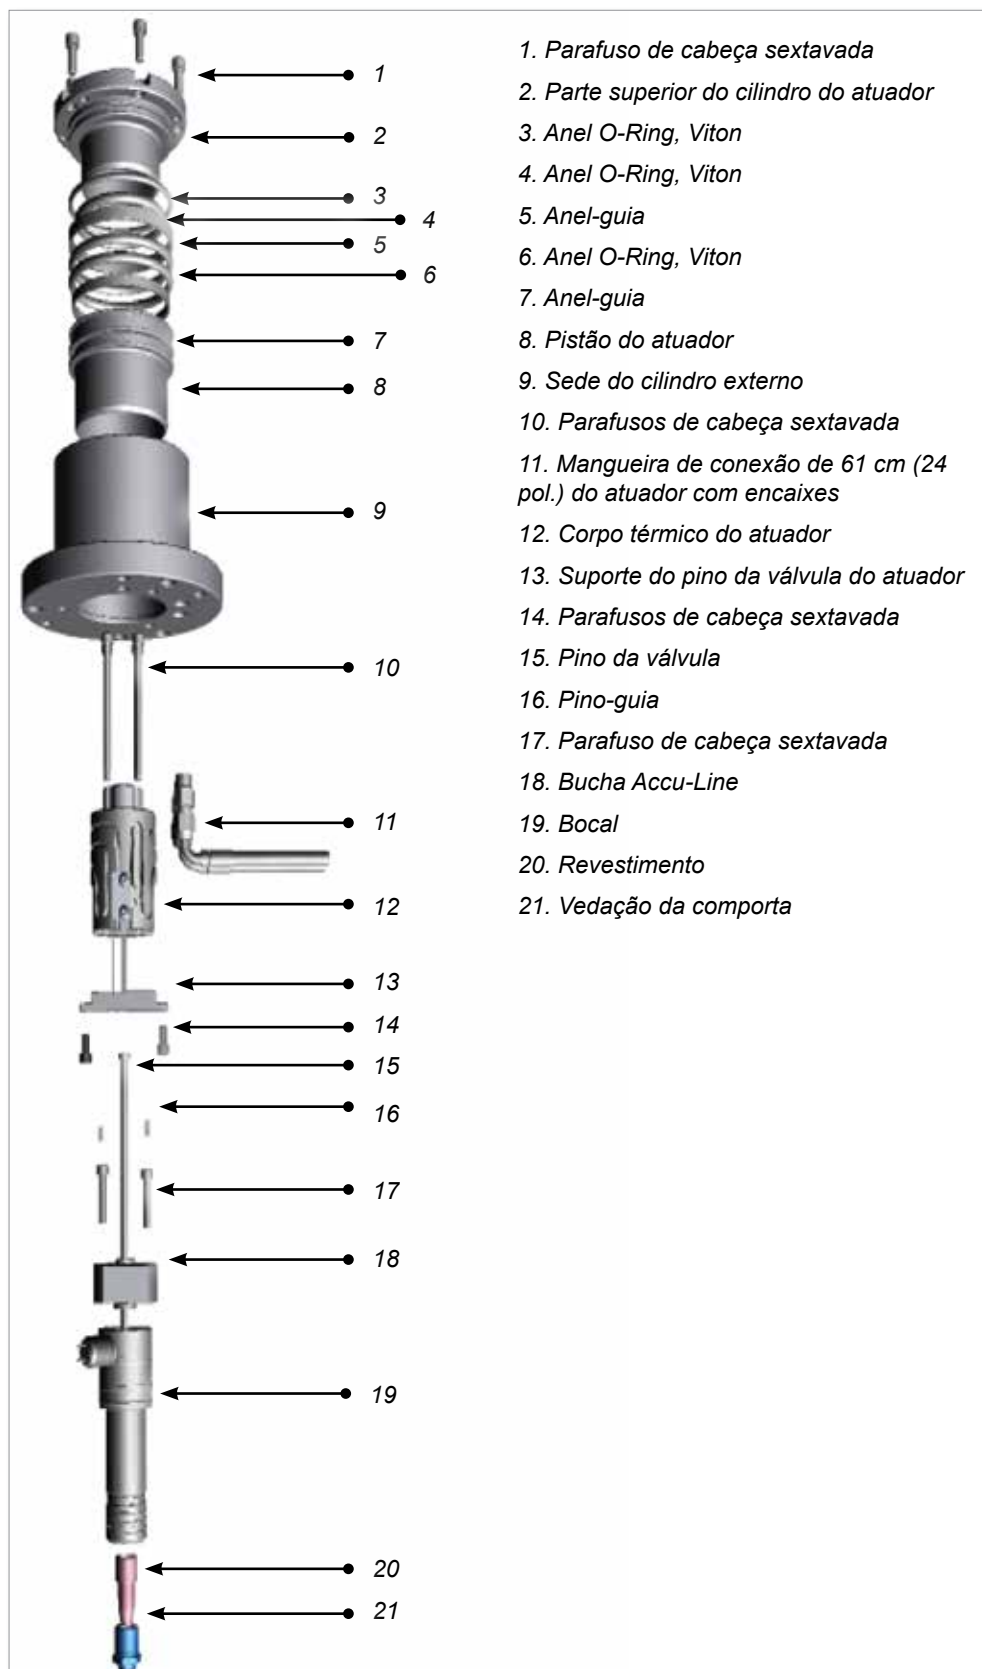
Conjunto do corpo do Centi Accu-Line
